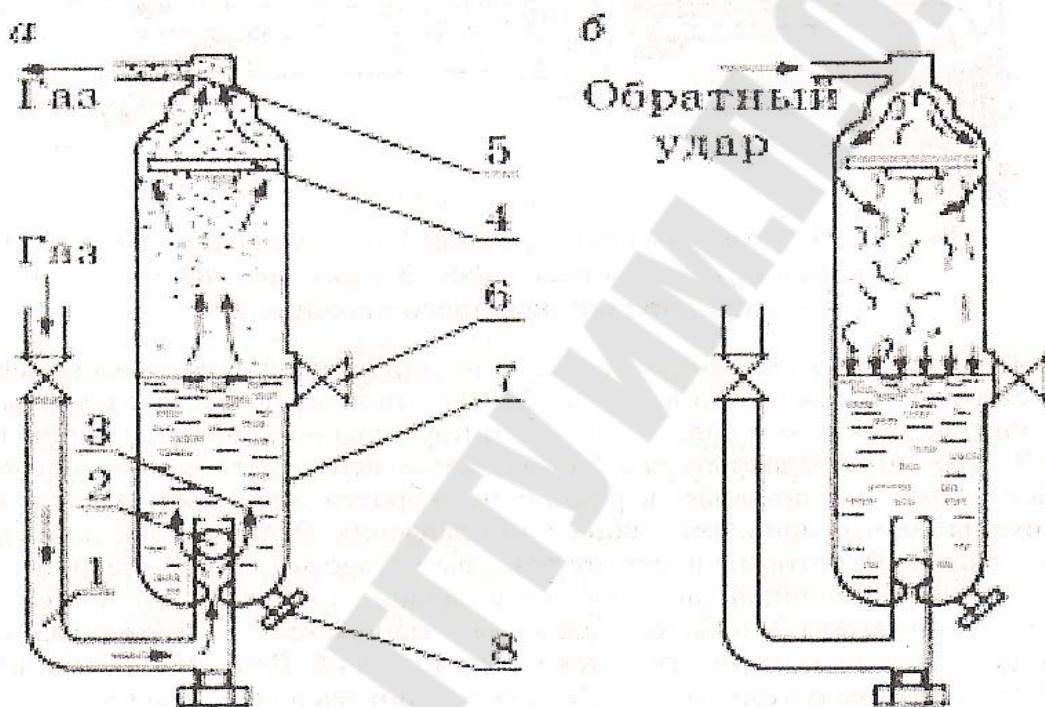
Схемы работы водяного затвора: а – при нормальной работе; б – при обратном ударе; 1 – трубка; 2 – обратный клапан; 3 – газ; 4 – диск; 5 – штуцер; 6 – контрольный клапан; 7 – корпус; 8 – сливной штуцер
